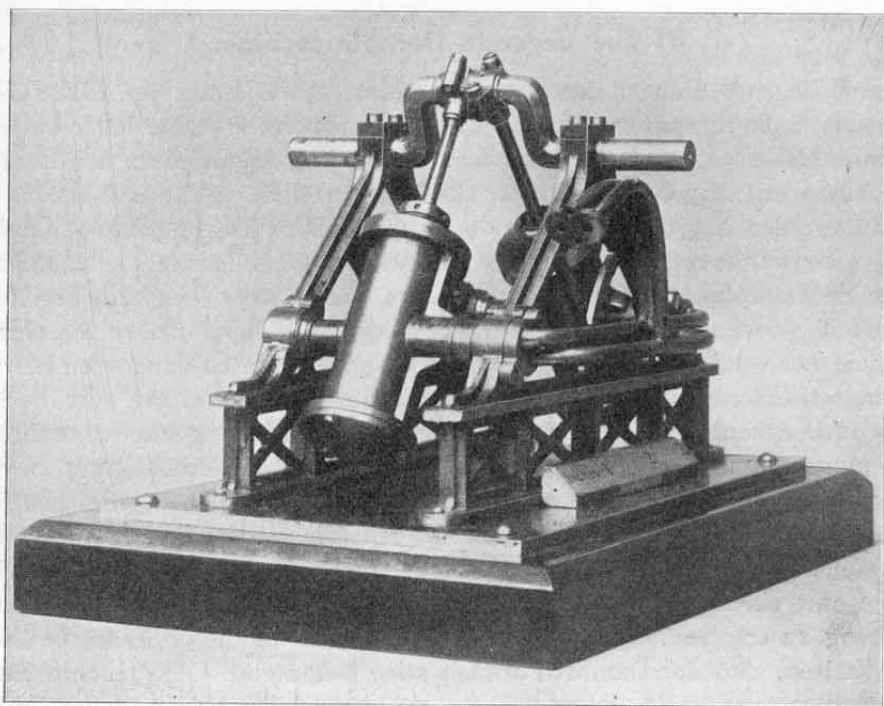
Oszillierende Zwillingmaschine Maudslay 1826.
